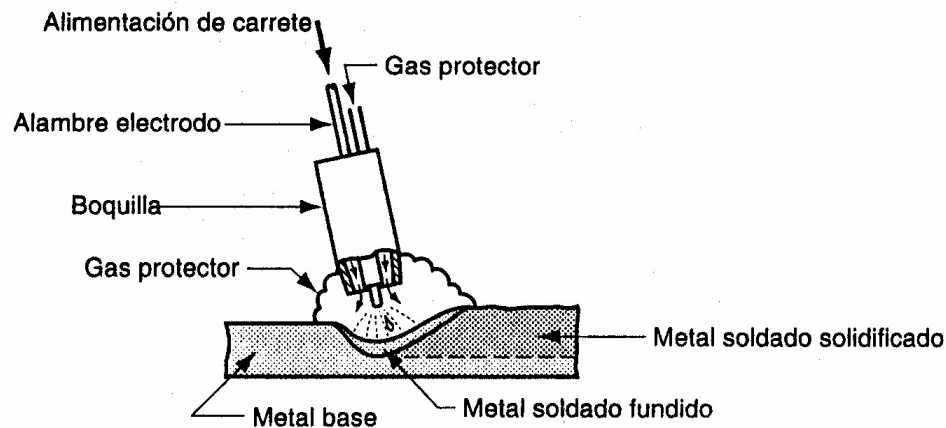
Soldadura metálica con arco eléctrico y gas (GMAW).
